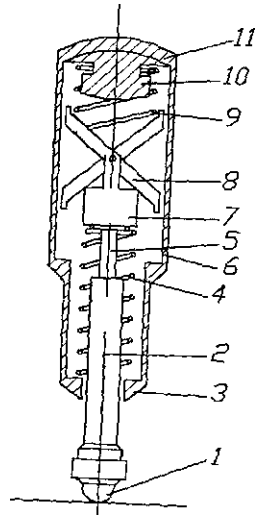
Принципиальное устройство прибора ПМ—2 (прибор в исходном состоянии): 1 — шарик (идентор); 2 — ударник; 3 — втулка; 4 — рабочая пружина; 5 — шток; 6 — корпус; 7 — боек; 8 — защелка; 9 — возвратная пружина; 10 — угорный вииг; 11 — задняя крышка
